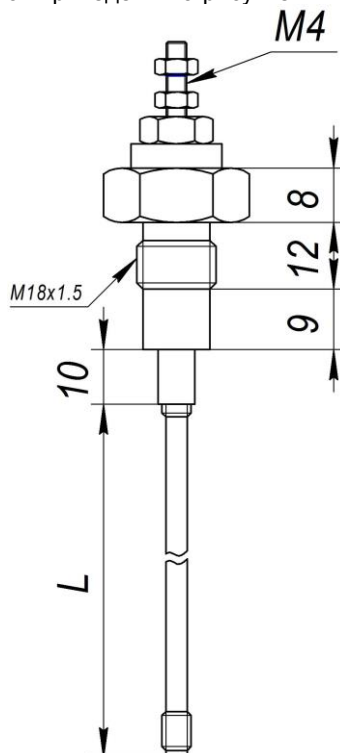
Внешний вид и габаритные размеры ДК-11
